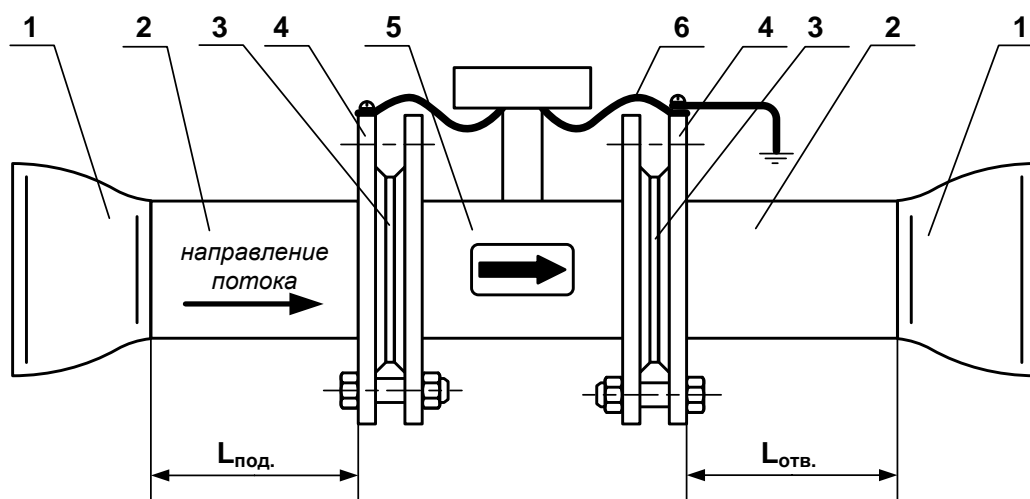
Вид сварки фланцев DN10, DN15, DN20 с переходным патрубком.
